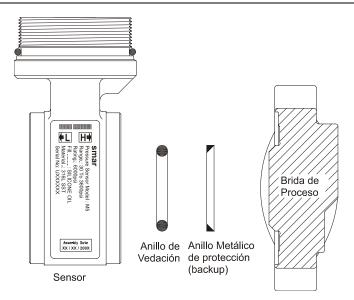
Montaje del anillo metálico de refuerzo (BACKUP)
